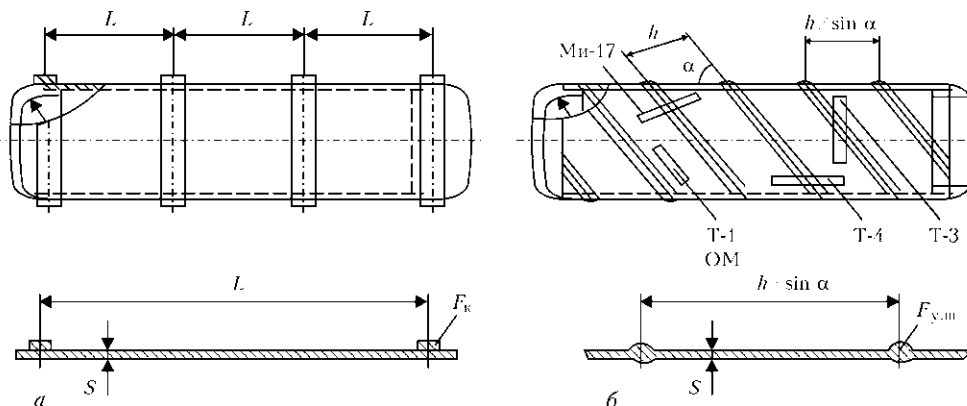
Схема вырезки образцов: *a* — корпус из тонкостенной трубы и бандажными кольцами; *б* — то же, но из СШТ; Т-1 — образцы из основного металла; Ми-17 — образцы сварного соединения с классическим расположением сварного шва; Т-4 — образцы Ми-18 с наличием сварного соединения в виде косога шва, вырезанные по образующей СШТ; Т-3 — образцы Ми-18 (специальные) с наличием сварного соединения в виде косога шва, вырезанные по радиальной поверхности СШТ; F_k , $F_{y,ш}$ — соответственно площадь сечения бандажного кольца и усиления шва
